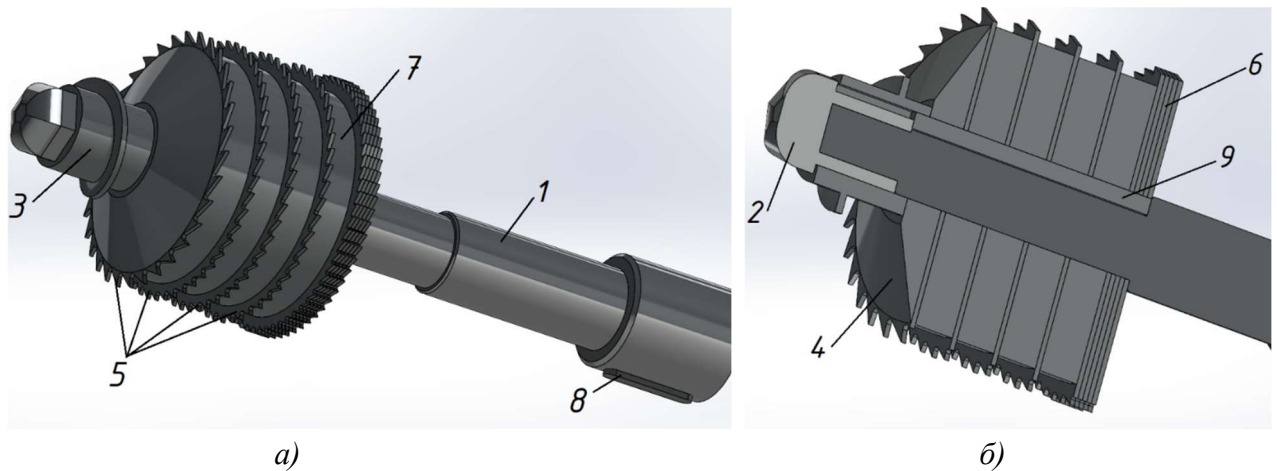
Вертикальный ротор в сборе (а); разрез ротора со шпонкой под режущую часть (б):
